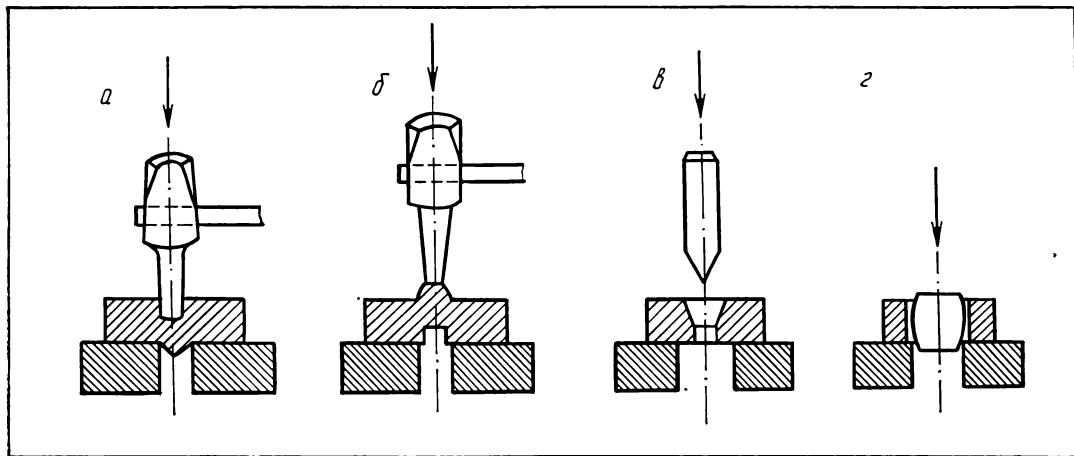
Пробивка и раздача отверстия в заготовке:
